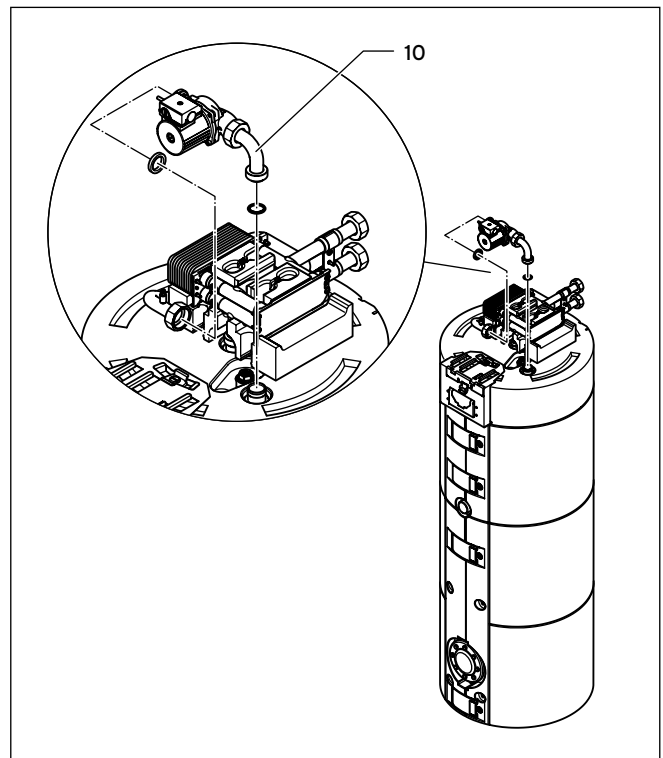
Montaggio della pompa di carica dell'acqua calda
